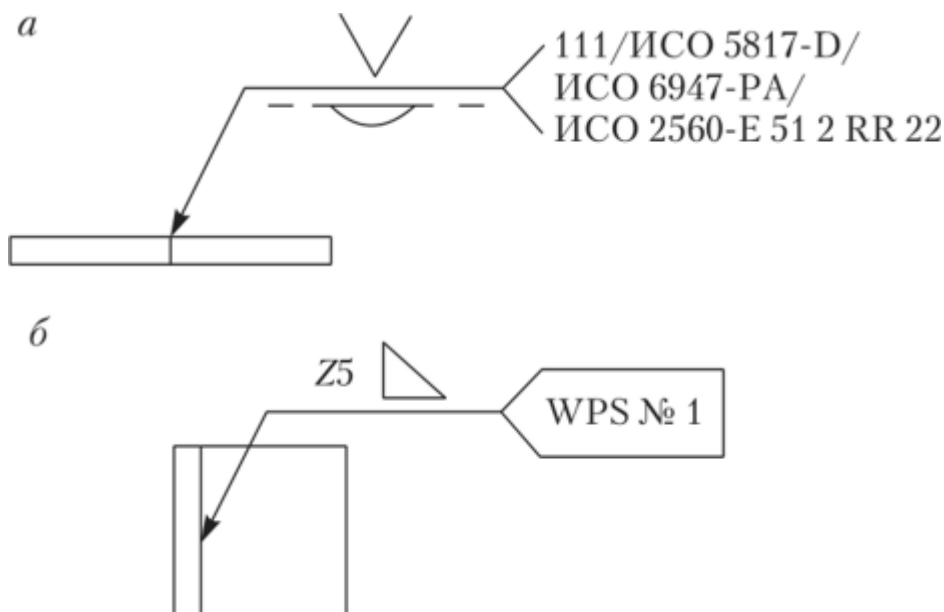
Варианты обозначения сварного шва по СТБ ISO 2553-2004:
